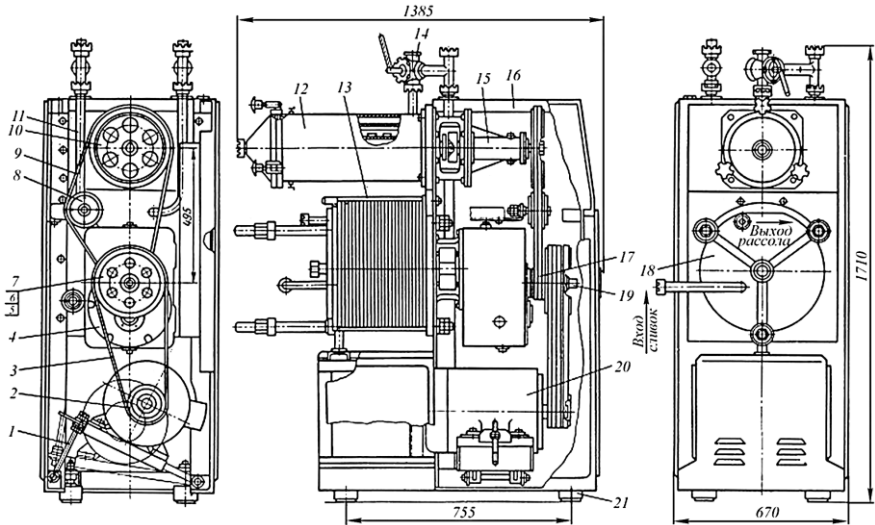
Загальний вигляд маслоутворювача марки РЗ-ОУА1: 1 - гвинт; 2, 5, 6, 7, 10, 17 - шків; 3 - ремінь Б-1600Т; 4 - редуктор; 8 - ролик натяжний; 9 - ремінь Б-1800Т; 11 - трубопровід; 12 - маслообробник; 13 - охолоджувач; 14 - кран триходовий; 15 - вал маслообробника; 16 - станина; 18 - плита нажимна; 19 - вал редуктора; 20 - електродвигун; 21 - опора
